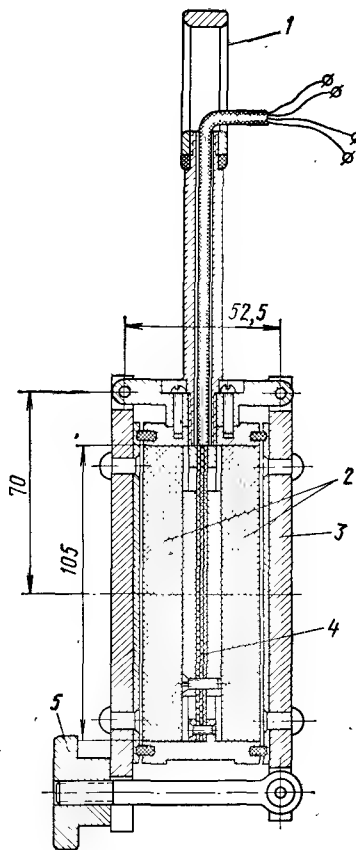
Плоский малогабаритный бикалориметр МПБ-64-1: 1 — рукоятка; 2 — испытуемые образцы; 3 — разъемный корпус; 4 — сердечник с нагревателем и батареей дифференциальных термопар; 5 — крепежный винт
